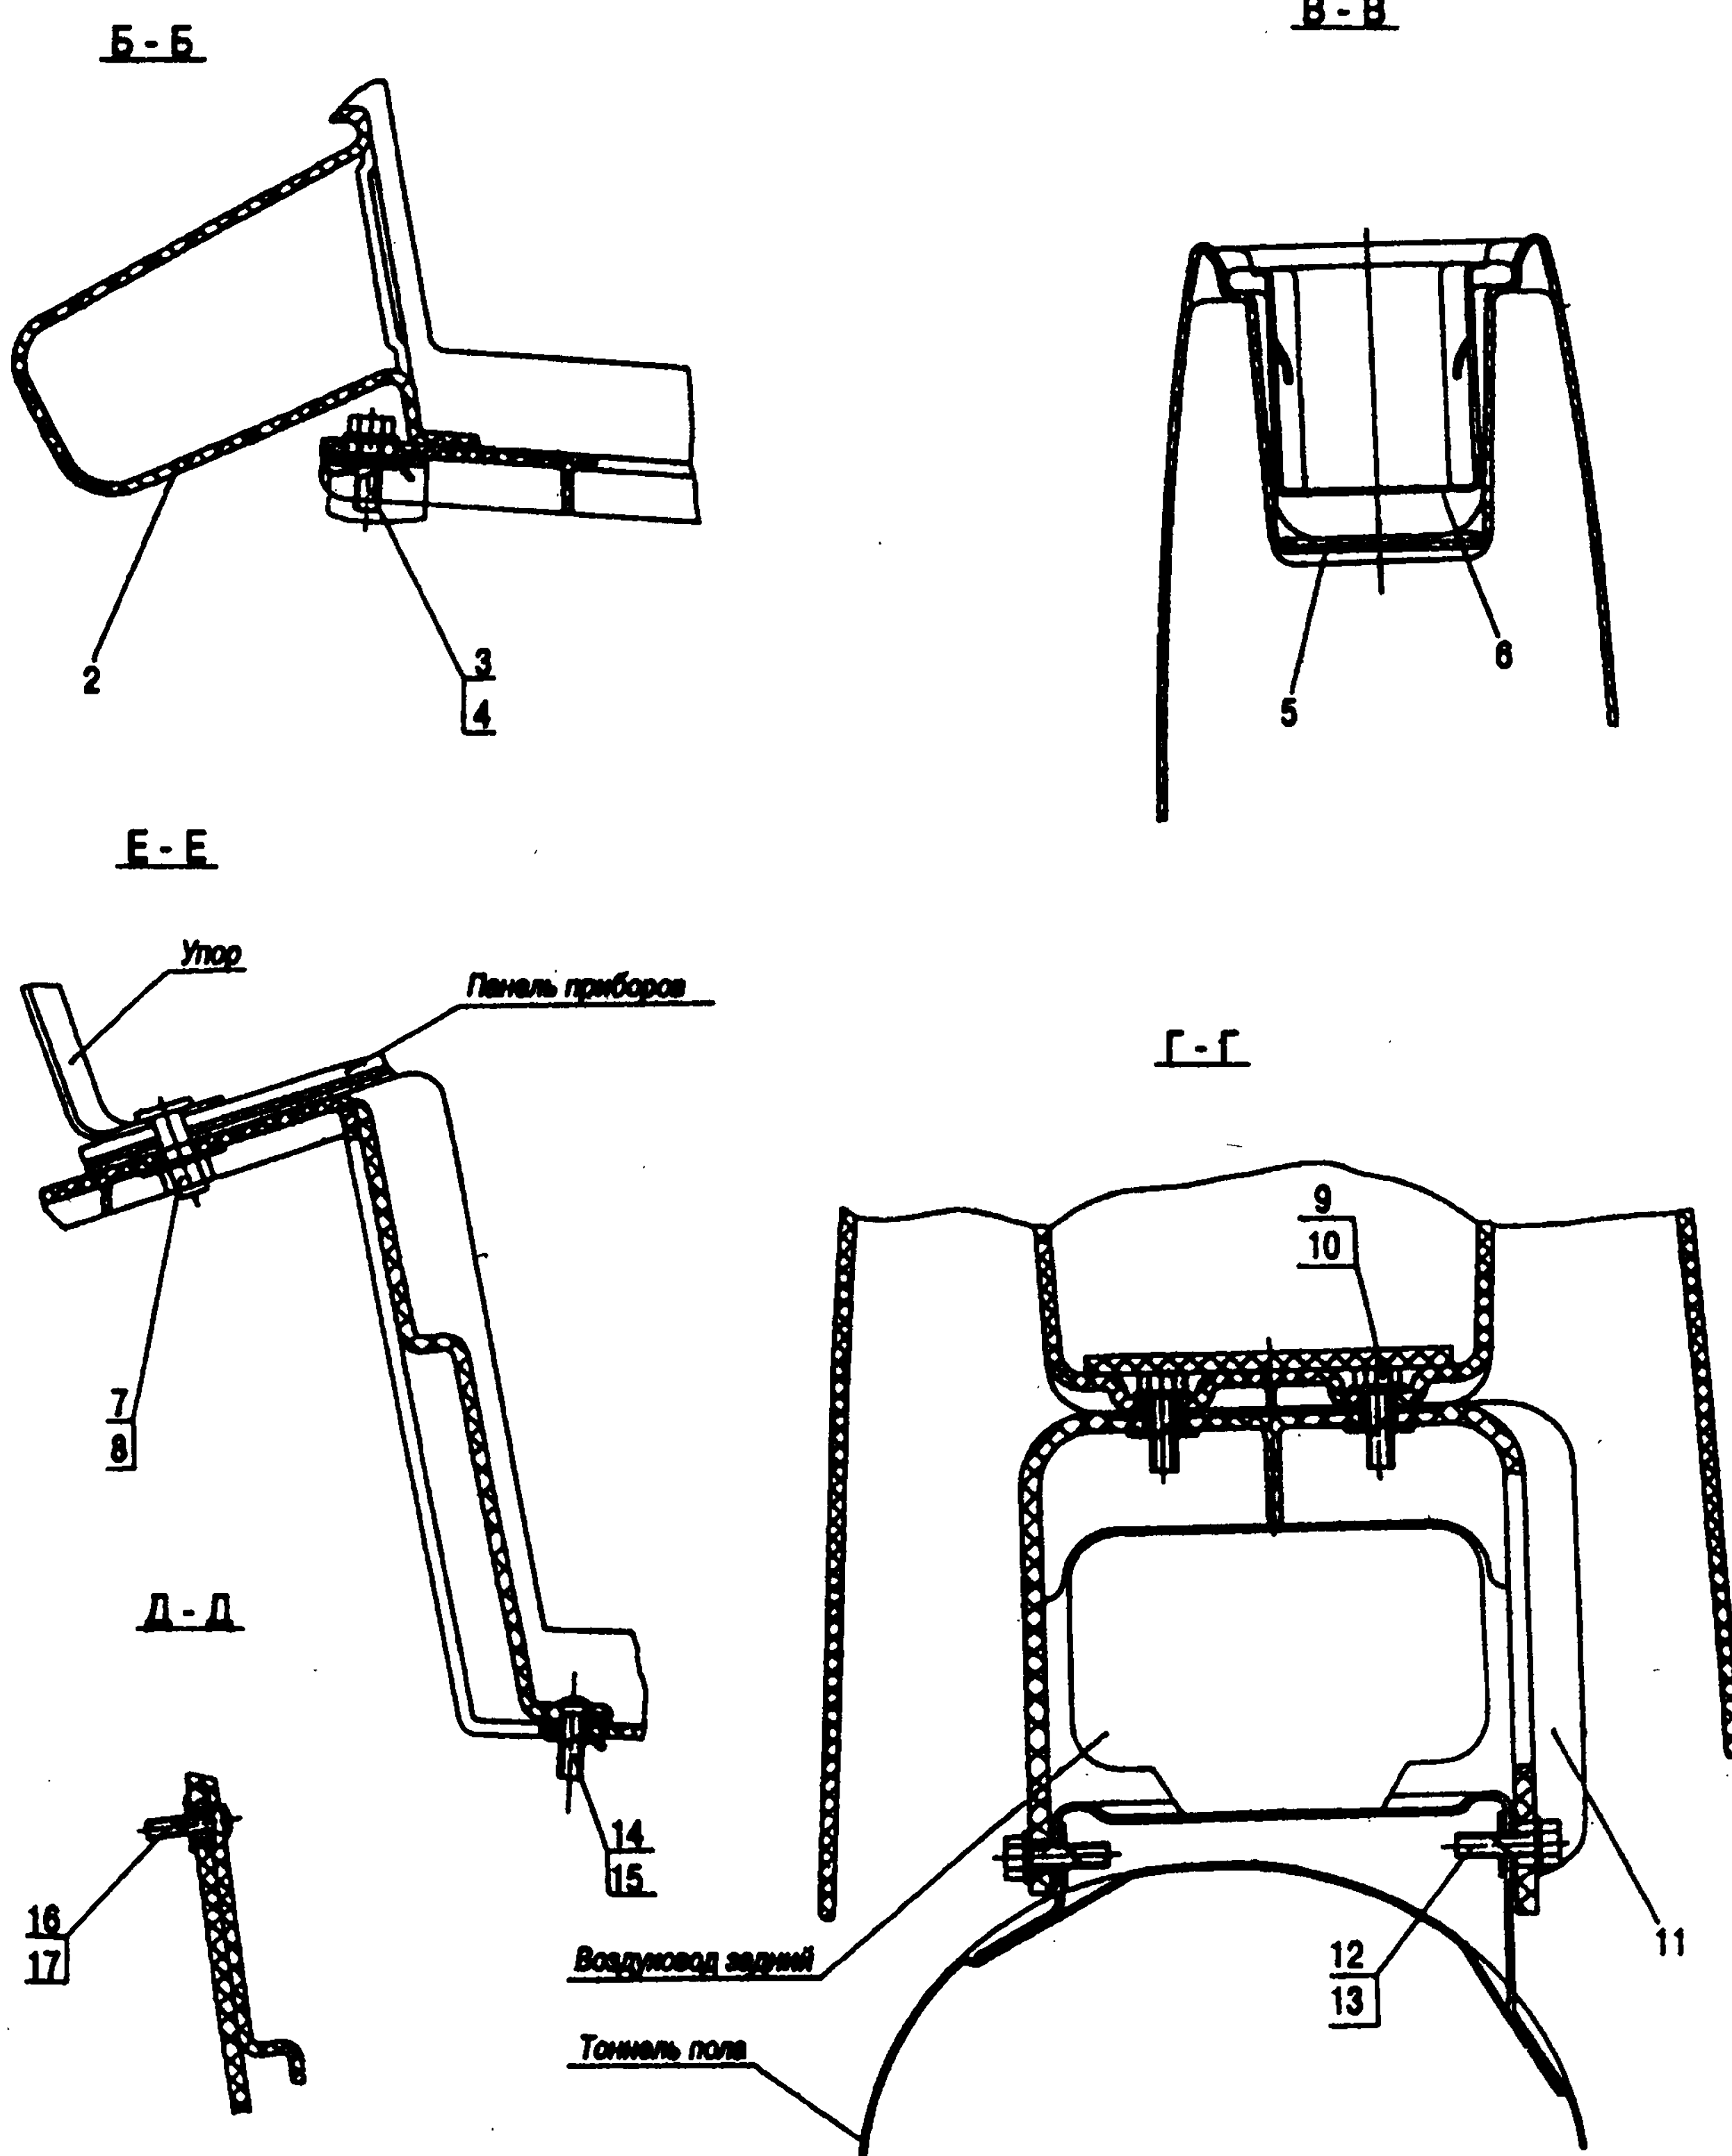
Консоль панели приборов. Точки крепления: 2 - пепельница; 3 - специальный винт; 4 - спец. гайка; 5 - вкладыш кармана подкассетника; 6 - подкассетник; 7 - гайка М6; 8 - шайба; 9 - специальный винт; 10 - специальная гайка; 11 - кронштейн консоли задний; 12 - специальный винт; 13 - специальная гайка; 14 - винт М6; 15 - специальная гайка; 16 - винт 4; 17 - специальная гайка
